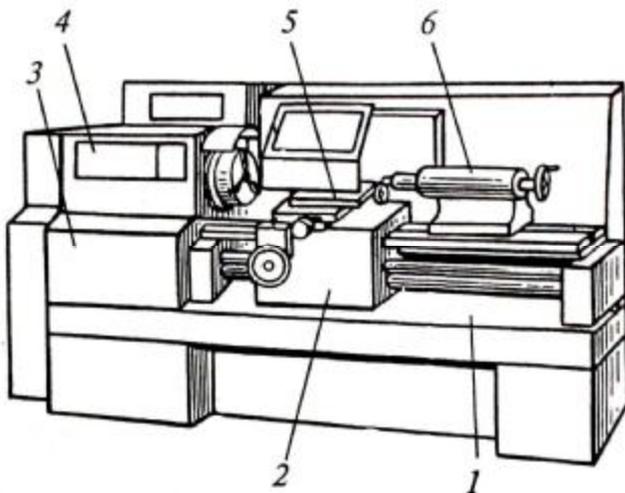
Токарно-винторезный станок (основные узлы): 1 – станина; 2 – фартук; 3 – коробка подач; 4 – передняя бабка; 5 – резцовая каретка; 6 – задняя бабка
